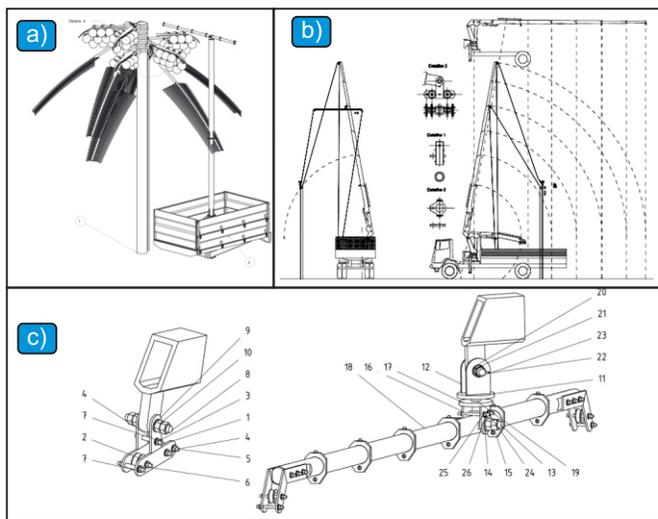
Coluna e viga de suporte da haste de auxílio a colheita a) Modelo da carreta b) Adaptação para a utilização do guindaste da unidade da Embrapa Instrumentação c) Desenhos do protótipo final construído.
